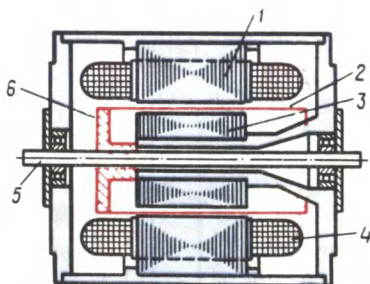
Асинхронный двигатель с полым немагнитным ротором:
